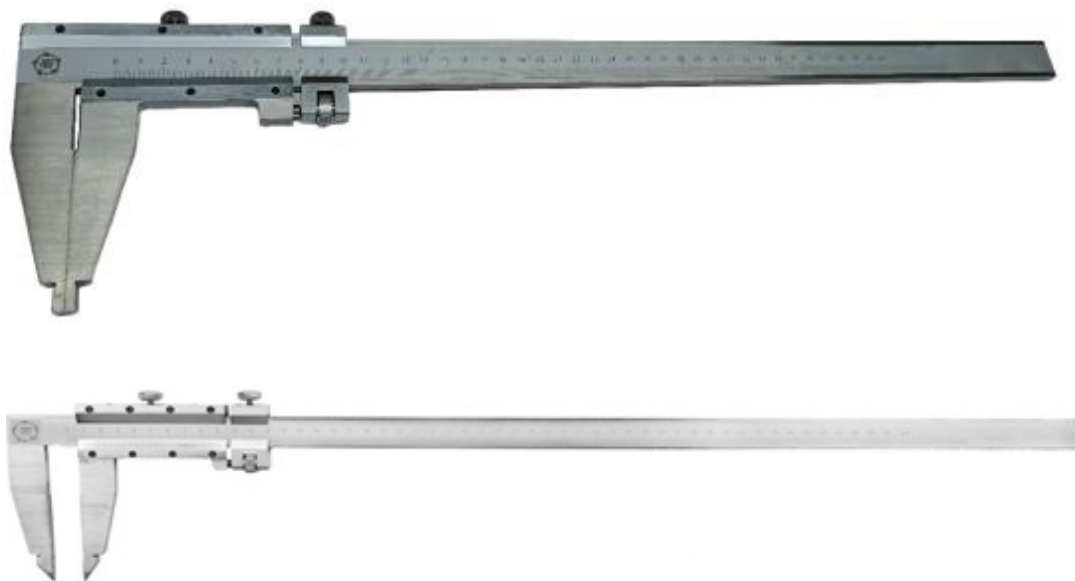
Общий вид штангенциркулей ШЦ типа III
